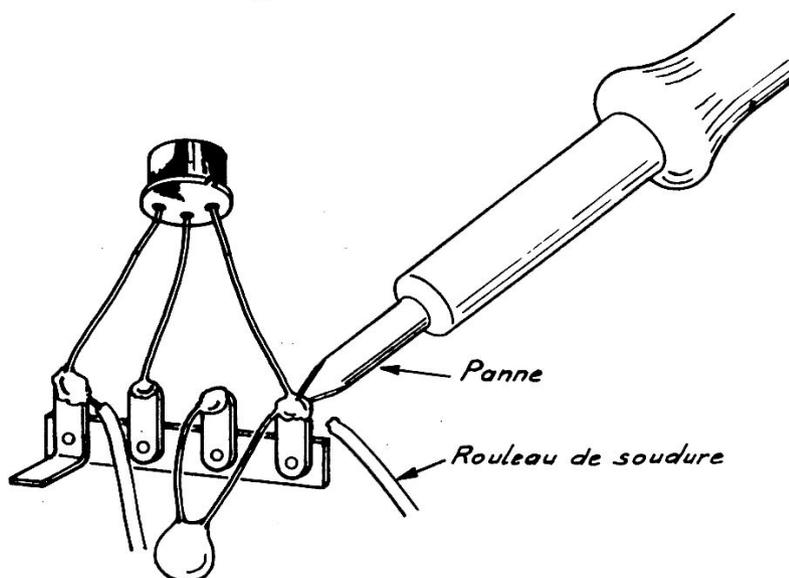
Un bon soudage : gage de bons contacts, d'un montage « qui marche »...
